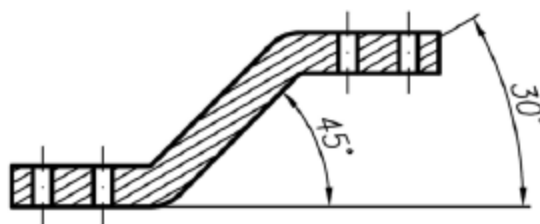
Element konstrukcyjny z oznaczeniem przekroju.
